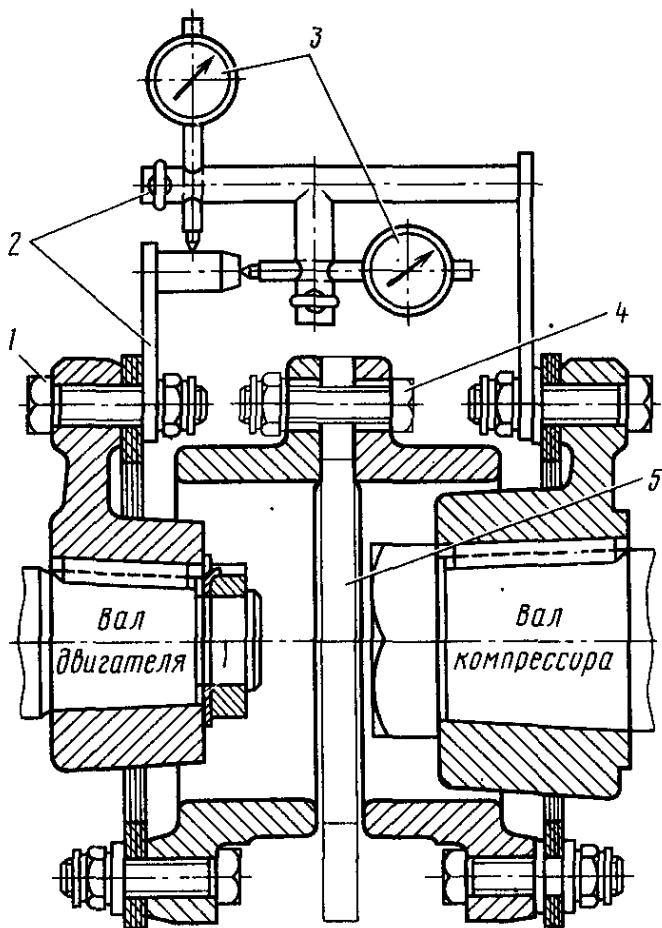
Приспособление для центровки валов двигателя НБ-431А и компрессора
